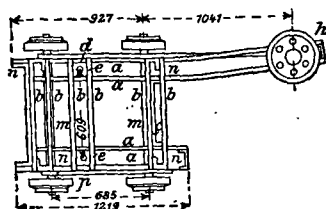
Testring de la coupelle américaine; coupe horizontale.
